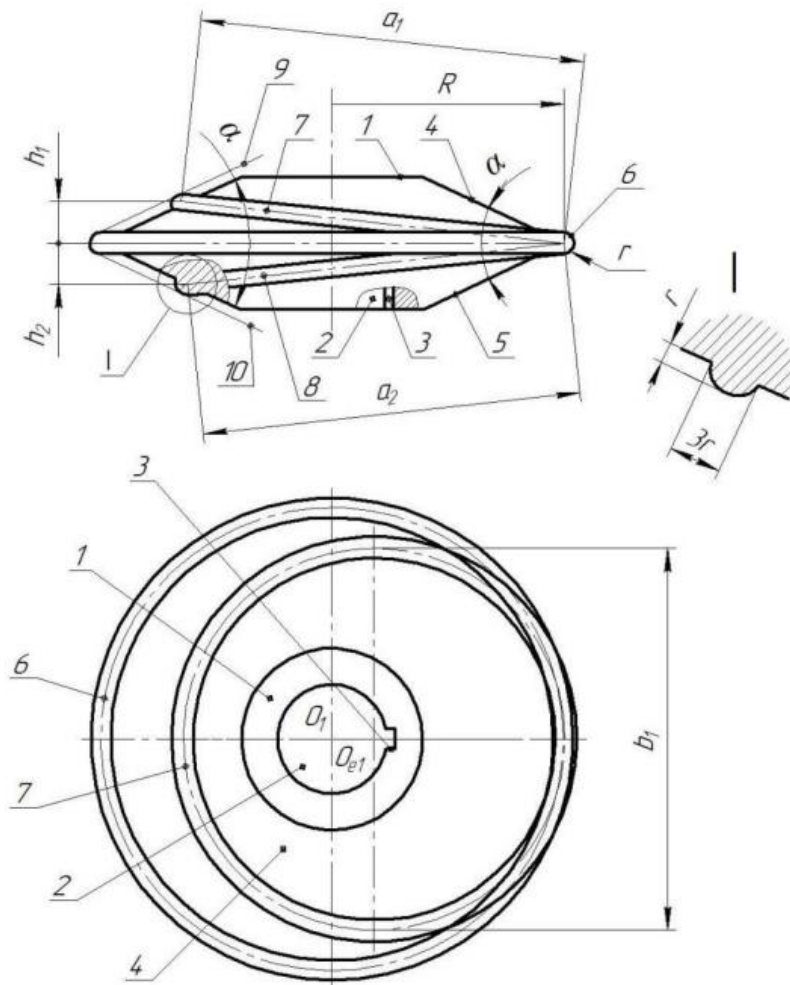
Інструмент для фрикційного зміцнення різьбових поверхонь [27]
